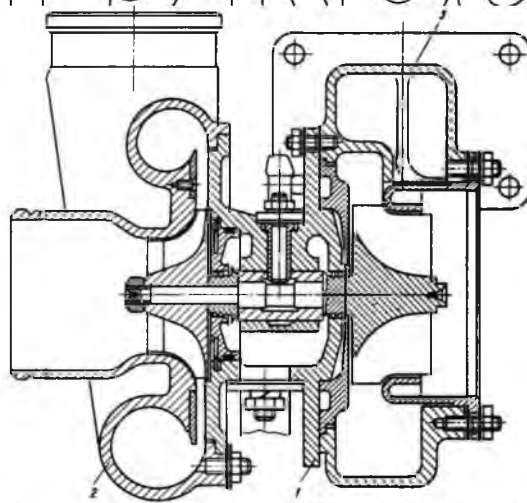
Компресорне устаткування типорозміру ТКР 9
